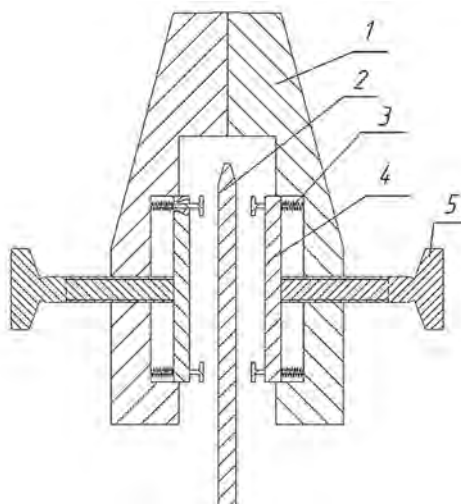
Схема защитного кожуха круглопильного отрезного станка
